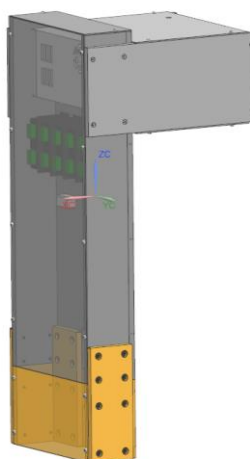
Porovnání půdní konstrukce kolébky s upravenou konstrukcí
